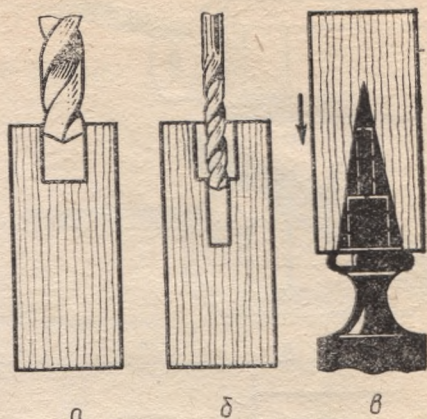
Насадка заготовки на хвостовик квадратного сечения с предварительным сверлением:
